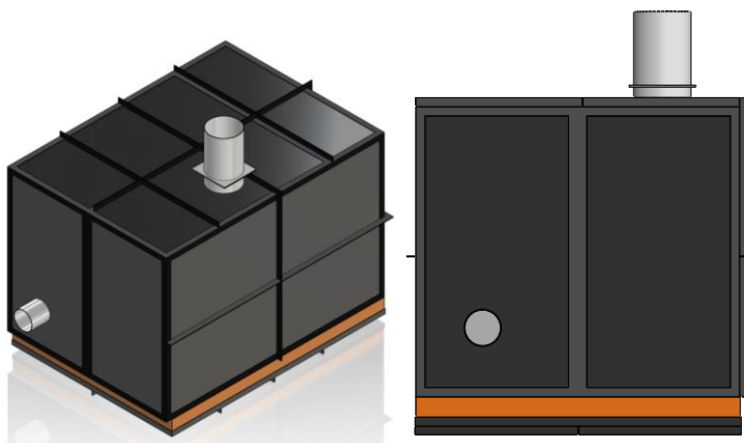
Ensamblaje del horno de secado en vista isométrica y frontal
